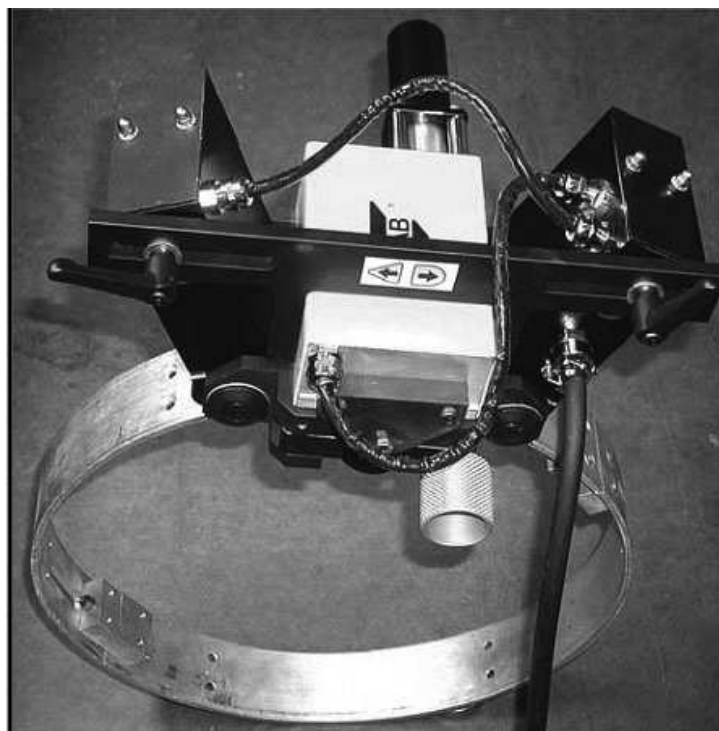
Сварочная каретка ESAB Railtrac Orbital W
